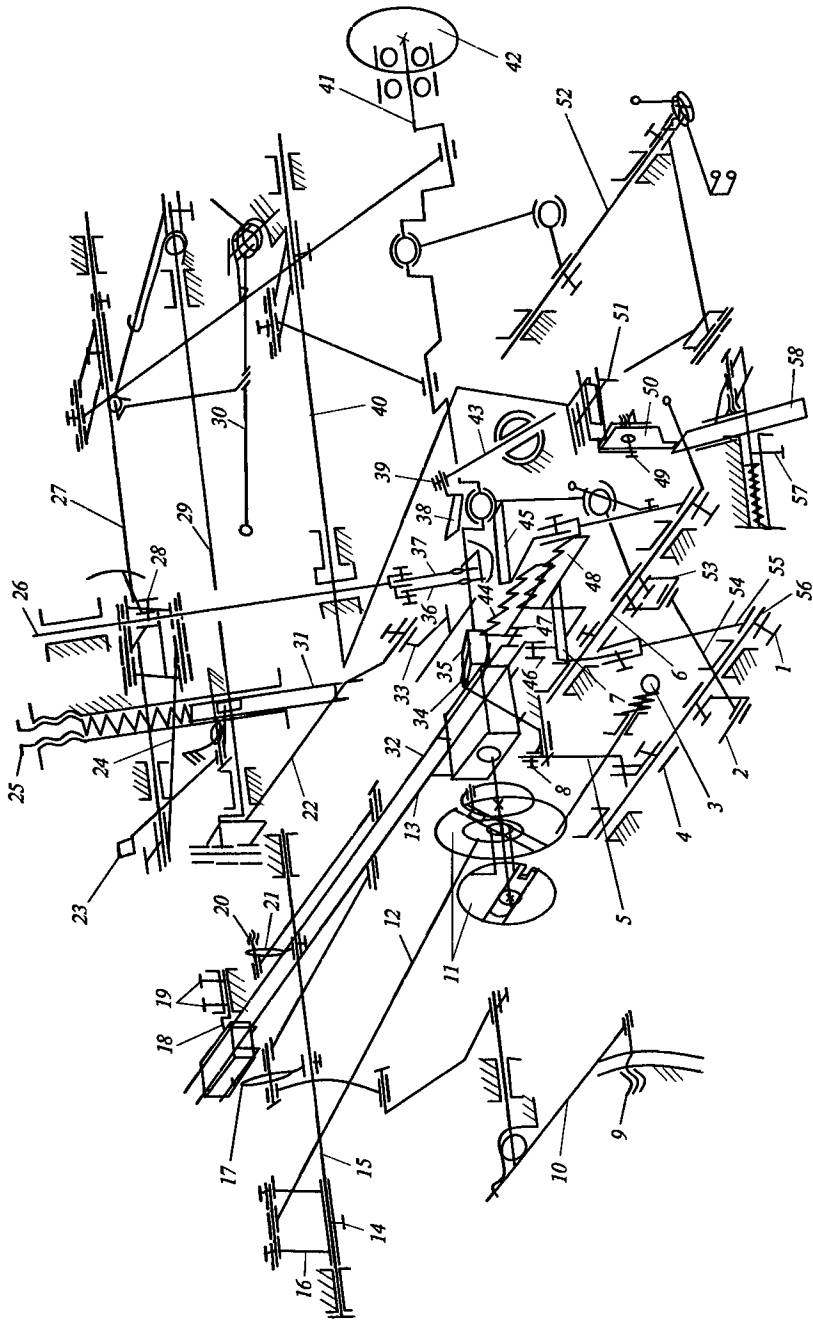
Кинематическая схема стачивающе-обметочной швейной машины класса GN2000-5 фирмы «Типикал»
